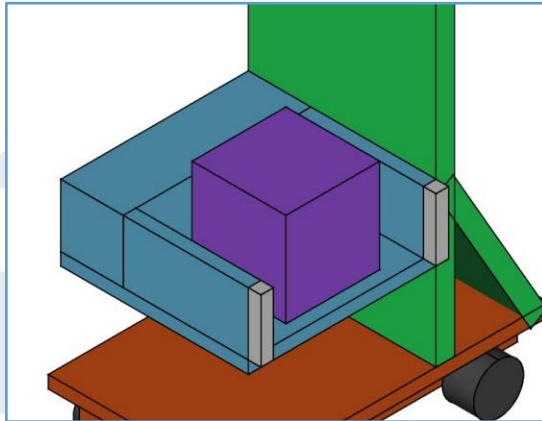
5 Deskripsi Tampak Samping AGV *Robot picker
